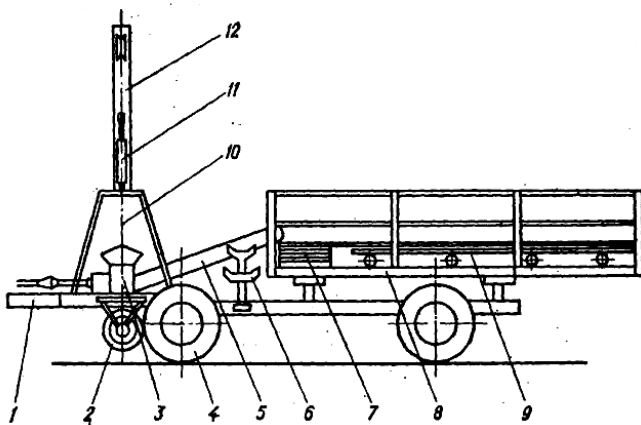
Схема широкозахватної платформи ПШ-25:
